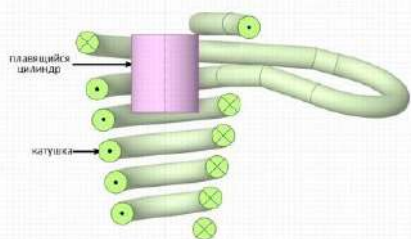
Модель конического индуктора с обратным витком и плавящейся заготовки в виде цилиндра
